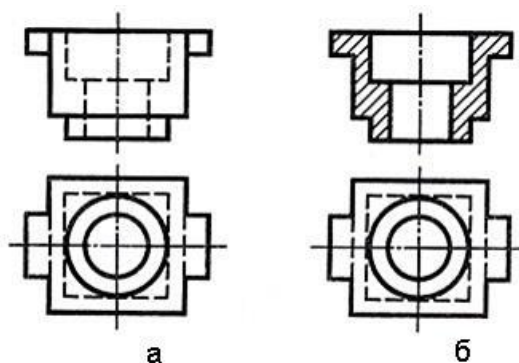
Чертеж детали без разреза (а) и с разрезом (б).
